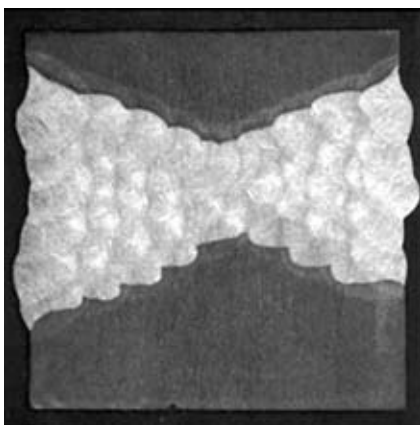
Микрошлиф сварного соединения стали толщиной 50,8 мм (2 дюйма), выполненного в горизонтальном положении способом сварки сдвоенным электродом
